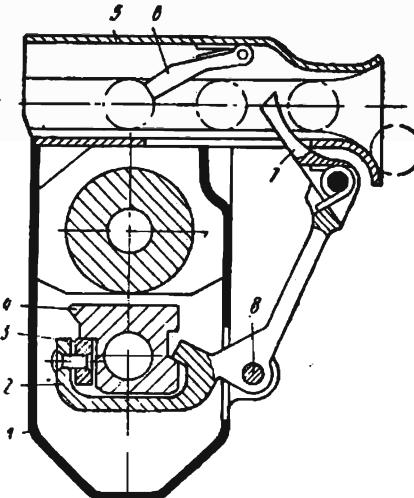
Конструктивная схема механизма подачи ленты качающимся рычагом:
